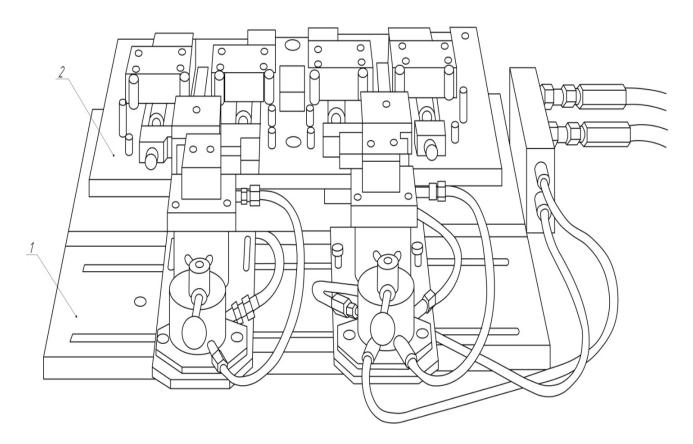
Специализированное наладочное многоместное приспособление для установки заготовок деталей типа «корпус – крышка»: 1 – базовая плита; 2 – сменная наладка
